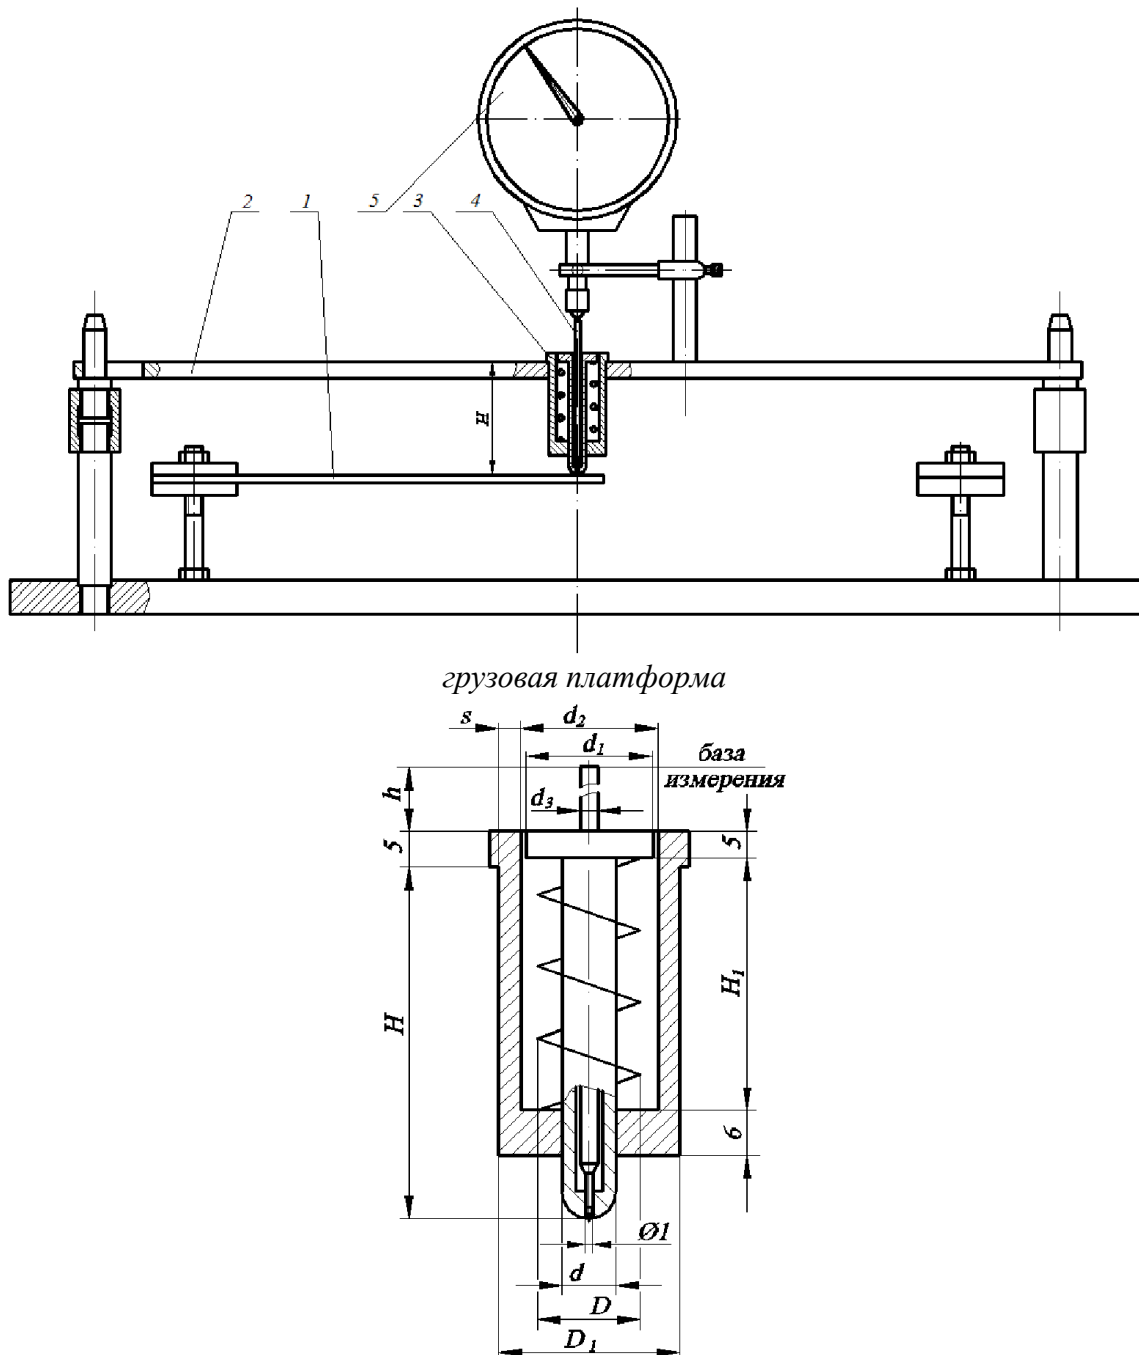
Нагрузочное устройство: 1 – балка, 2 – установочная рама; 3 – грузовая платформа; 4 – измерительный щуп; 5 – индикаторная головка
